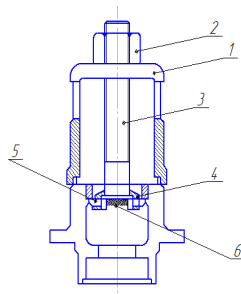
Съемник для выпрессовки обойм с помощью кулачков на пружинах
